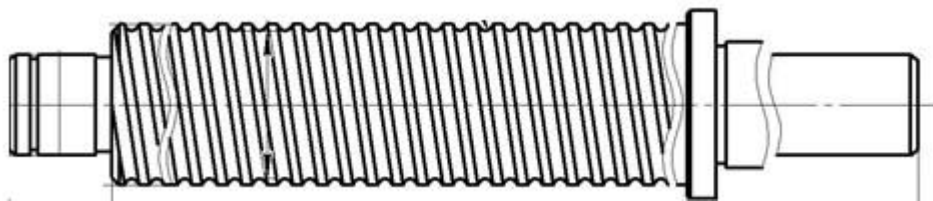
Ходовий гвинт приводу токарного верстату
